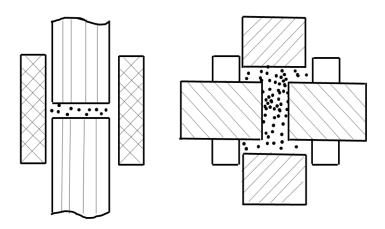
Возможные схемы диффузионной сварки деталей с применением порошковых промежуточных прослоек: а- сварка стержней встык; б-сварка листов встык.
